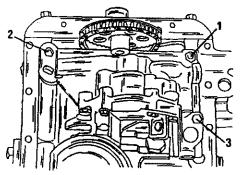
Расположение болтов крепления масляного насоса. Болты имеют различную длину.
